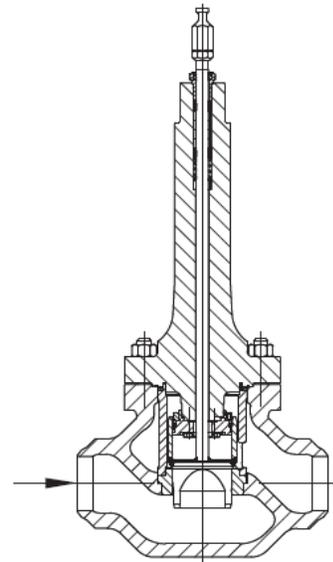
· Клапан типа 3291 с концами под приварку и изолирующей вставкой
